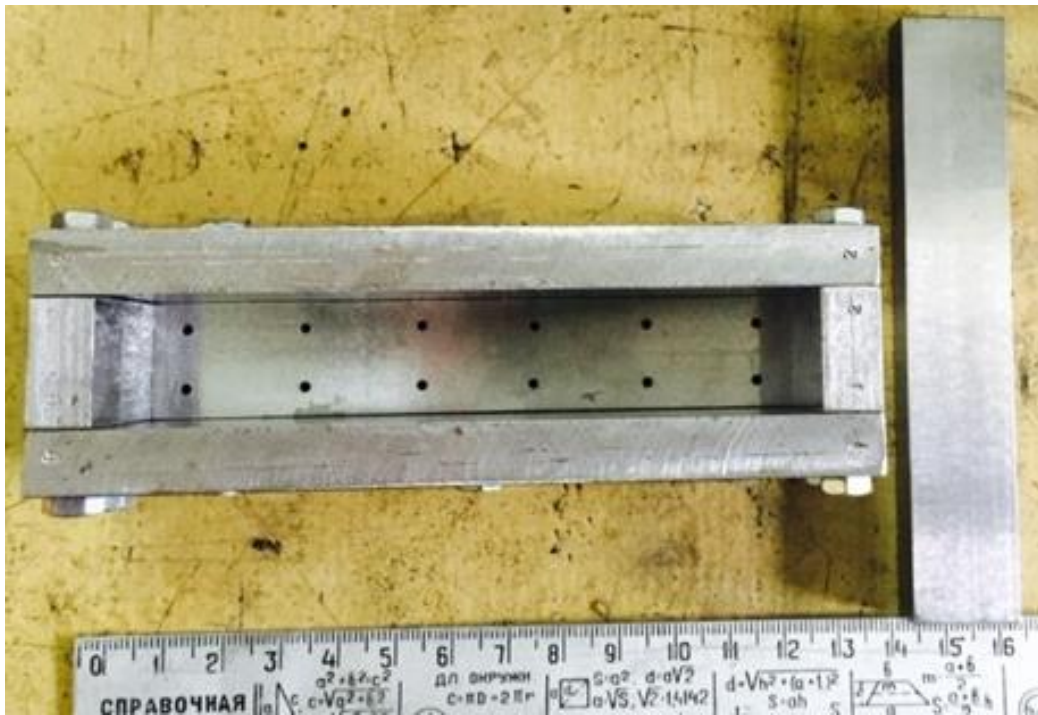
Общий вид пресс-формы для изготовления зарядов ГРД
